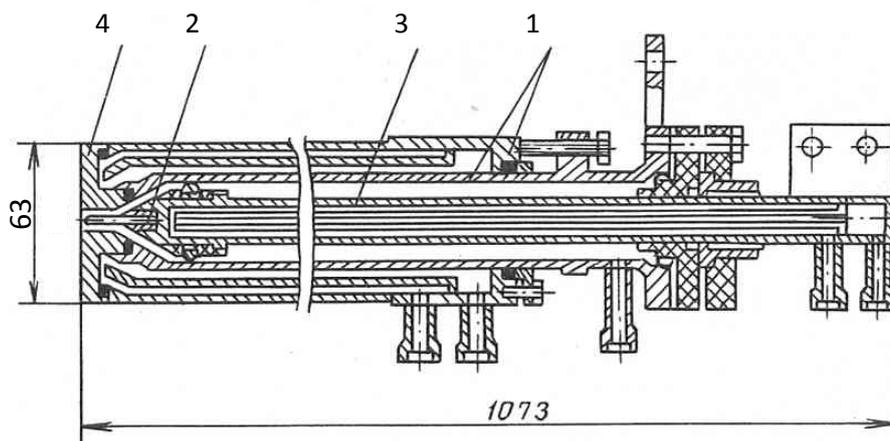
Плазмотрон ПТП-25М для плавки и переплава чёрных и цветных металлов. 1 – корпус, 2 – катод, 3 – катододержатель, 4 – сопло (вспомогательный электрод)
